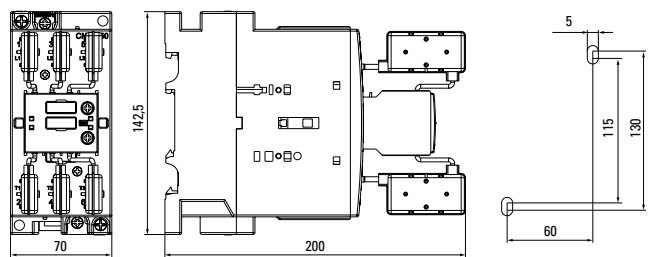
Габаритные и установочные размеры контакторов КМЭК 75
